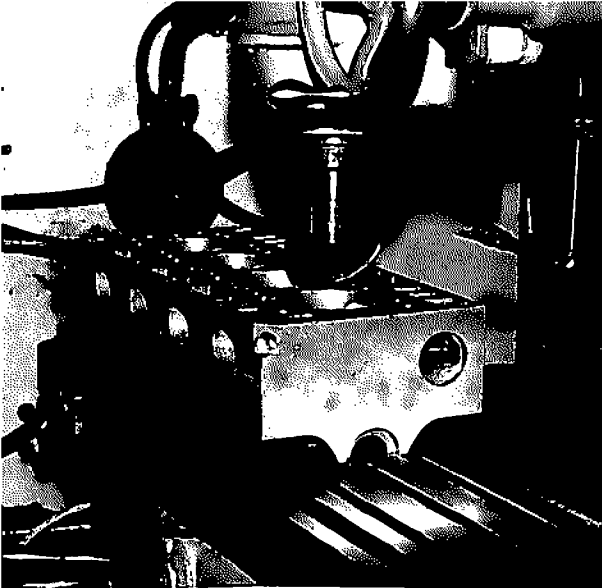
Ausdrehen der kugeligen Brennraumform mittels Formmesser auf der Vertikalfräsmaschine.
